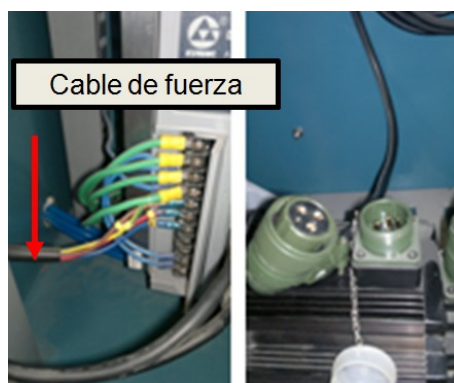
Cable de fuerza para la conexión servo drive - servo motor.
